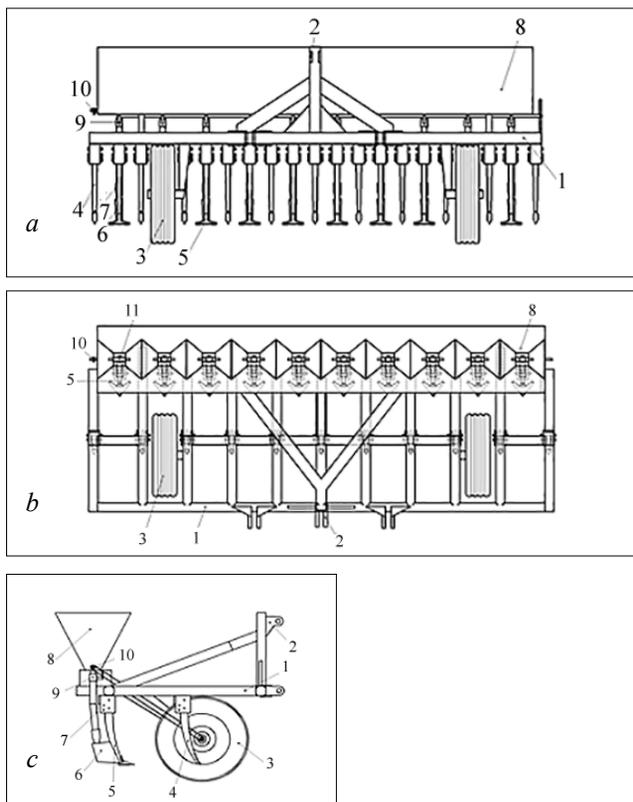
Схема агрегата для вынесения минеральных удобрений в ходе предпосевной обработки почвы: а – вид спереди; б – вид сверху; с – вид сбоку; 1 – рама агрегата; 2 – навеска рамы; 3 – опорное колесо; 4 – стойки с узкими рыхлительными лапами; 5 – стойки со стрельчатыми лапами; 6 – сошники для вынесения минеральных удобрений; 7 – трубопровод для минеральных удобрений; 8 – бункер; 9 – регулятор поступления минеральных удобрений; 10 – заслонка трубопровода; 11 – измельчитель
